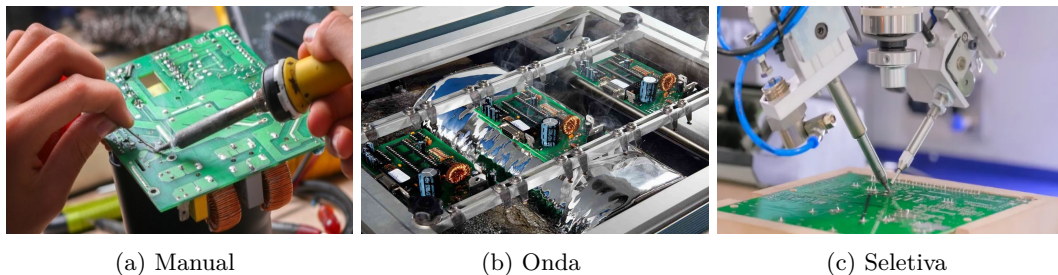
Tipos de soldadura no processo THT; adaptado de [97], [98], [99].
